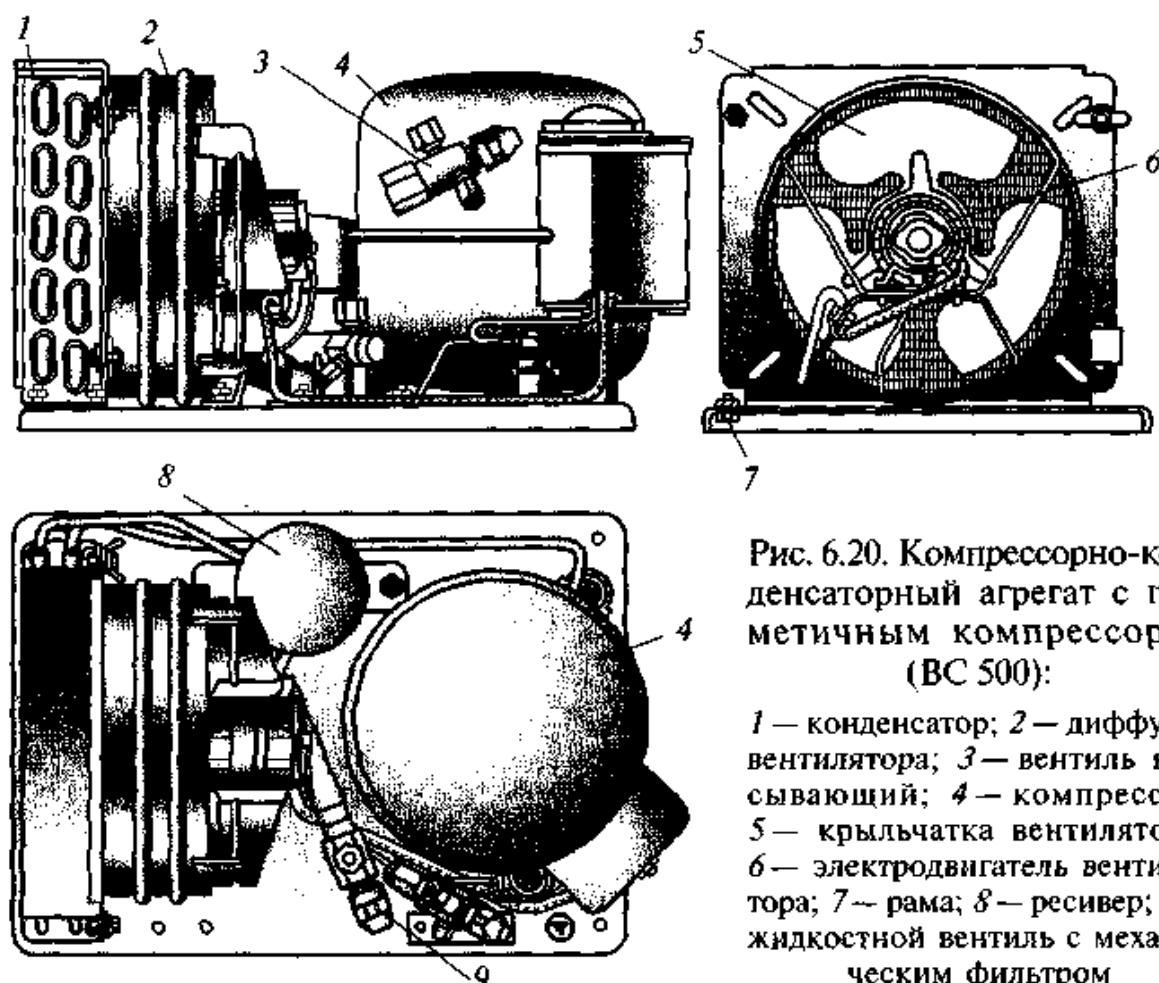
Компрессорно-конденсаторный агрегат с герметичным компрессором (ВС 500):
